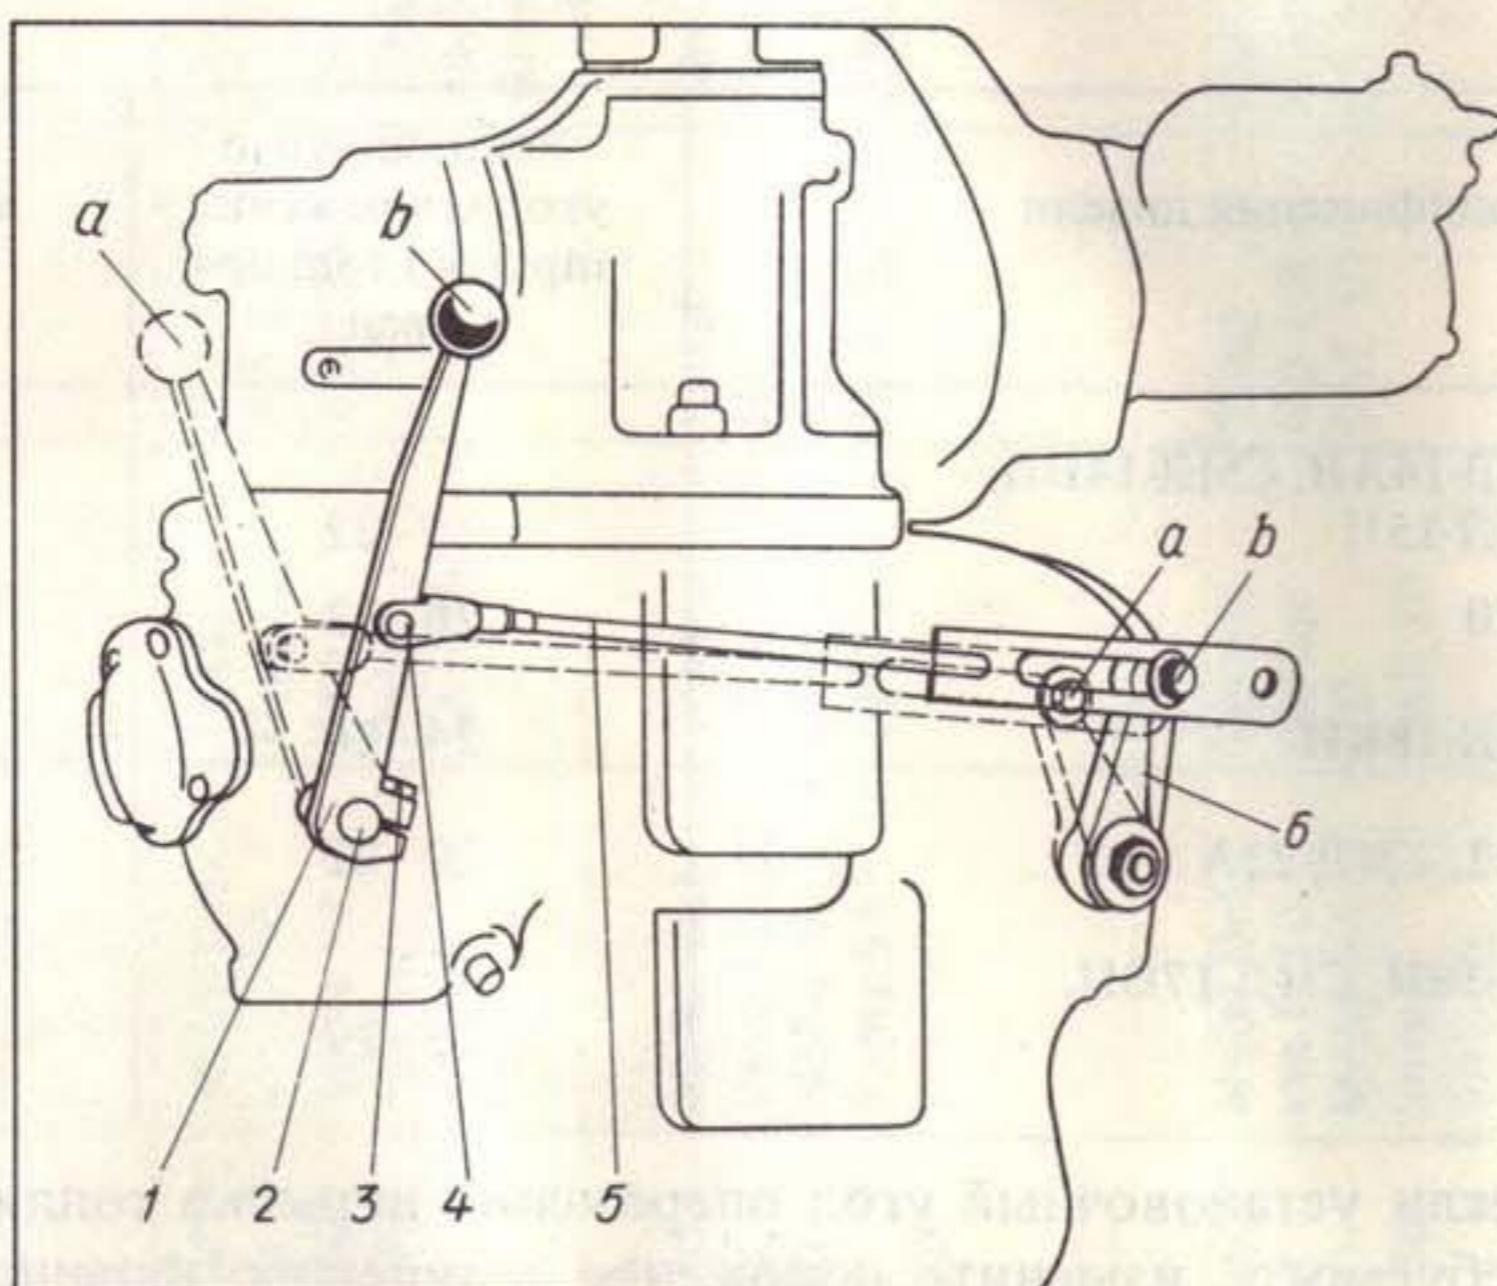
Рычаги управления редуктором пускового двигателя:
